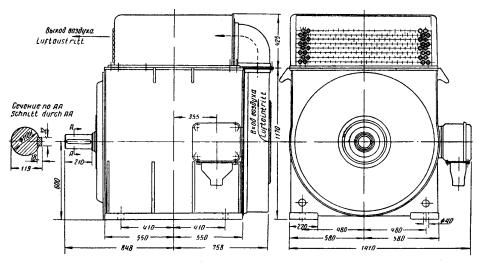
Габаритные размеры асинхронного двигателя ДАЗО-14 Abb. 2. Außenmaße des Asynchronmotors ДАЗО-14
